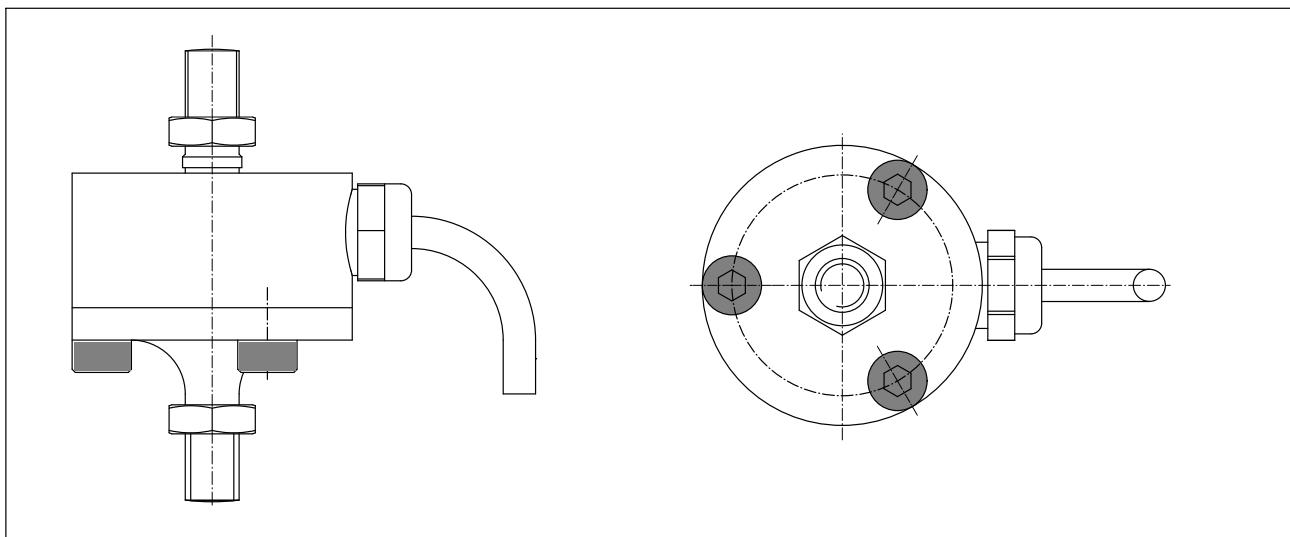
Adapterbefestigung mit drei Schrauben
